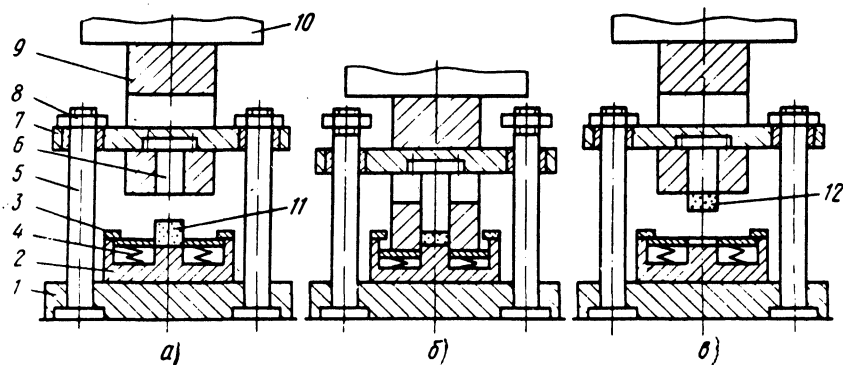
Схема ДГП деталей в штампах с верхним расположением матрицы
